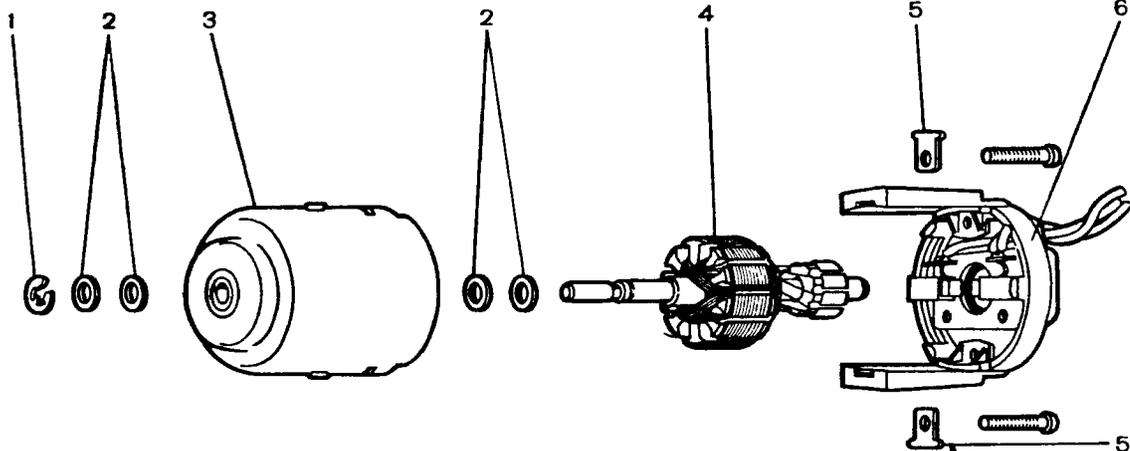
Детали электродвигателя отопителя: 1 - стопорная шайба; 2 - шайбы; 3 - корпус; 4 - якорь; 5 - сухари; 6 - крышка
